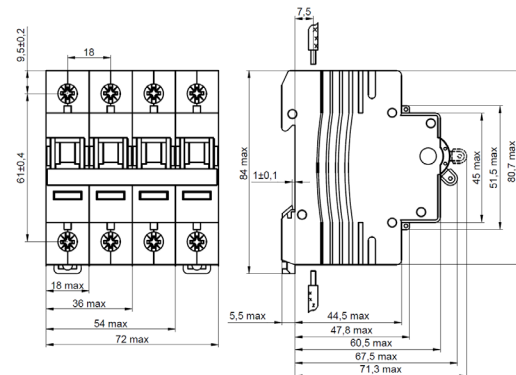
Габаритные, установочные, присоединительные размеры выключателей.
